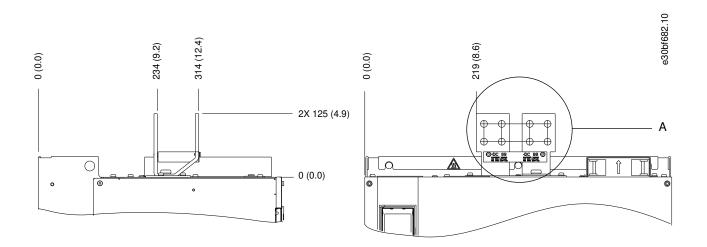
Dimensions des bornes réseau, moteur et de terre E4h (vues latérales)
